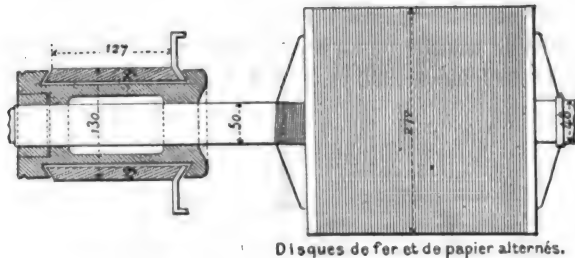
Machine Edison-Hopkinson. — Induit.
